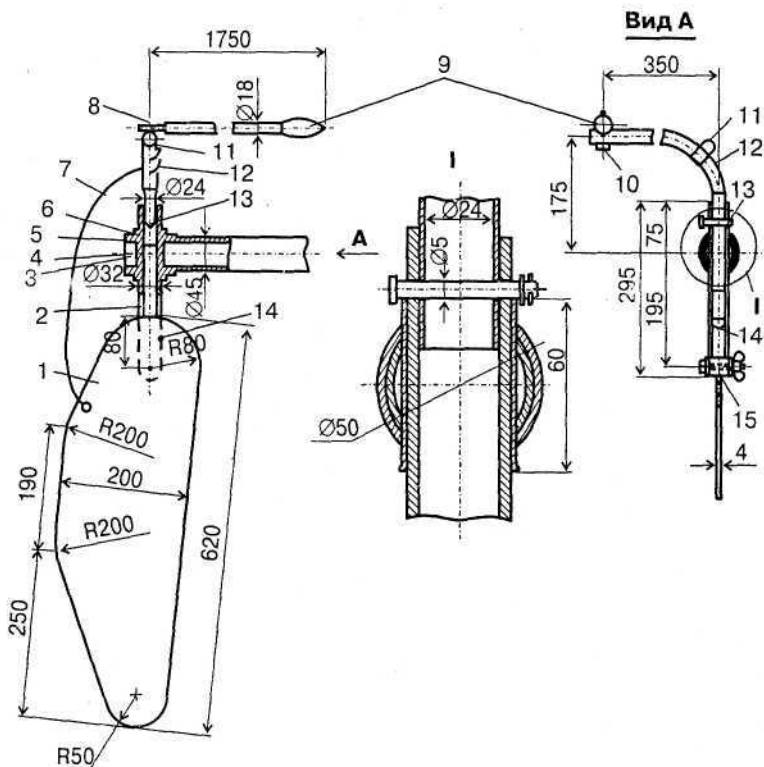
Руль: 1 — перо руля, дюралюминий; 2 — баллерная труба 32×4; 3 — заклепка $\varnothing 3$; 4 — центральная балка; 5 — баллерная накладка, труба 50×2,5; 6 — усиливающая втулка, нержавеющей сталь, труба 34×1; 7 — сорлинь; 8 — шплинт $\varnothing 3$ мм; 9 — удлинитель румпеля, труба 18×1; 10 — соединяющий палец $\varnothing 8$ мм; 11 — скоба крепления сорлиня; 12 — руппель, труба 24×1; 13 — ограничитель $\varnothing 6$ мм; 14 — ограничитель поворота руля $\varnothing 5$ мм; 15 — ось-болт руля М8
